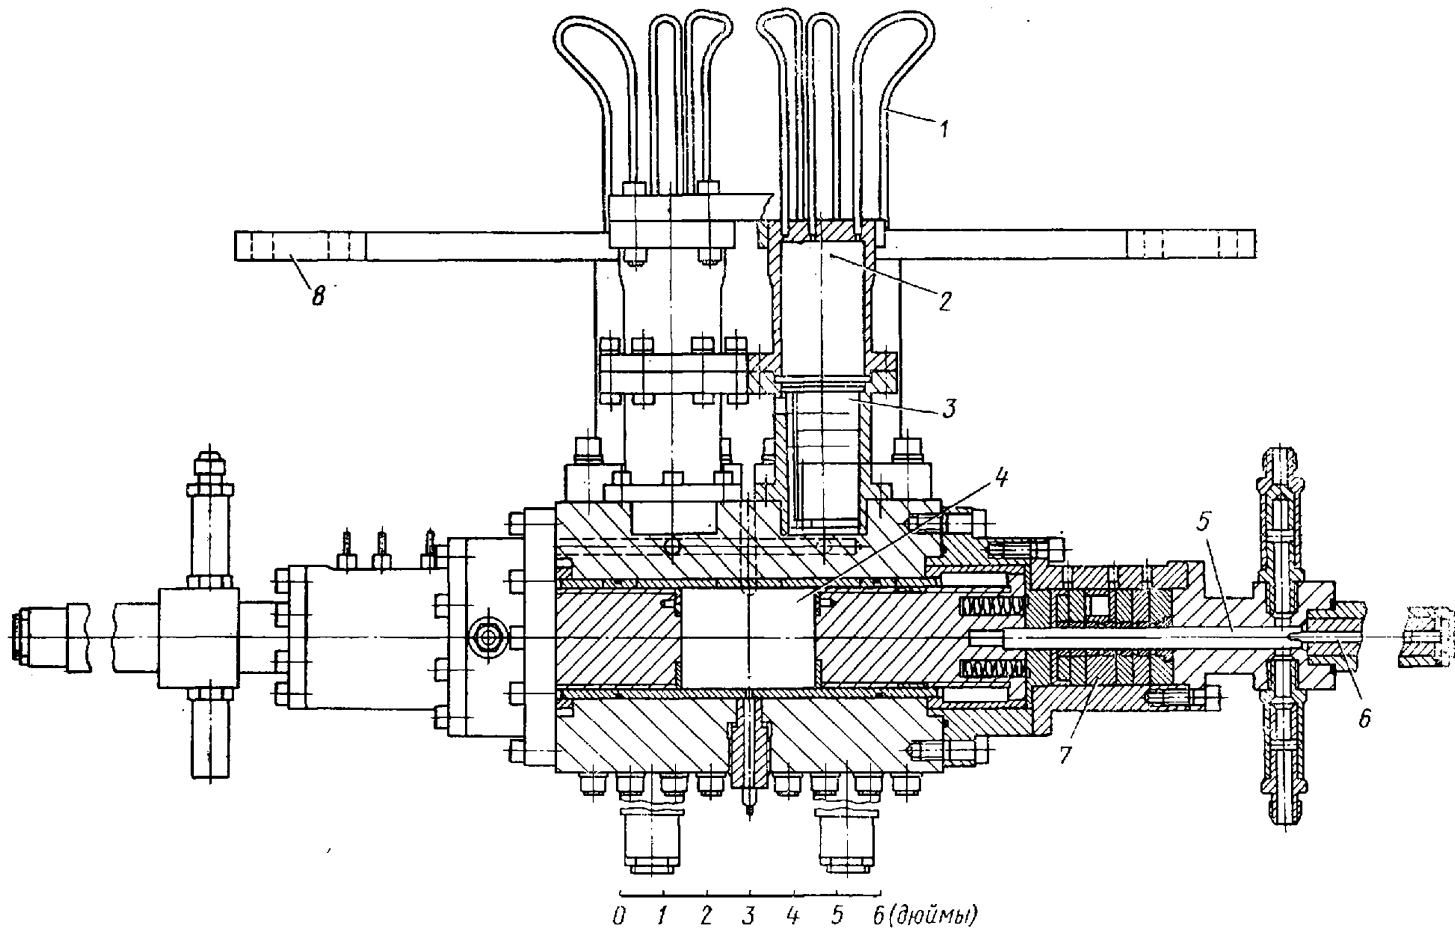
Свободнопоршневой двигатель Стирлинга с гидростатическим приводом:
